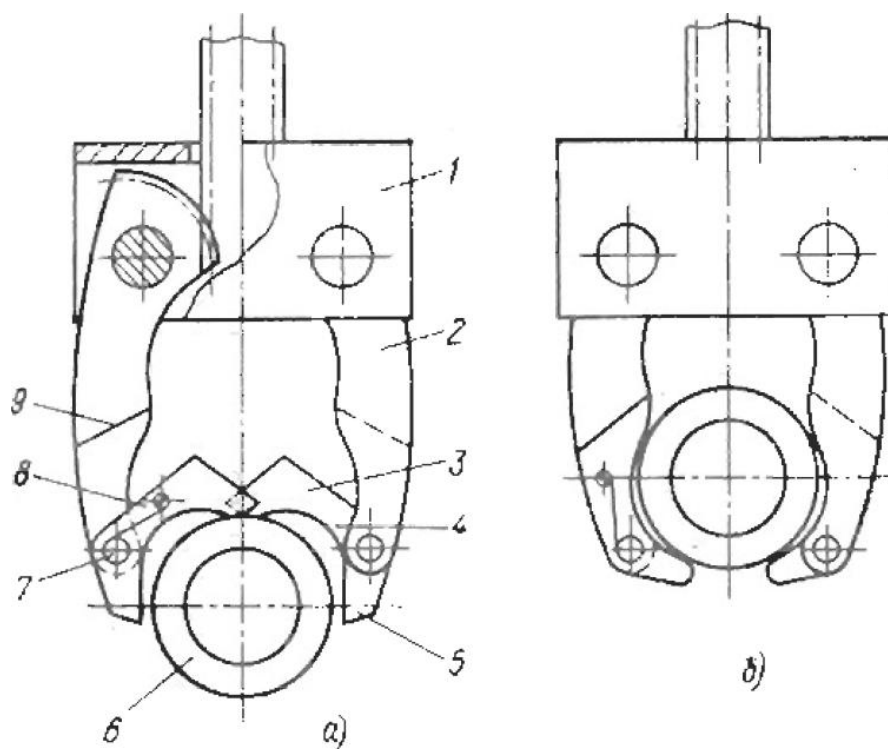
Захватное устройство: а – исходное положение;
